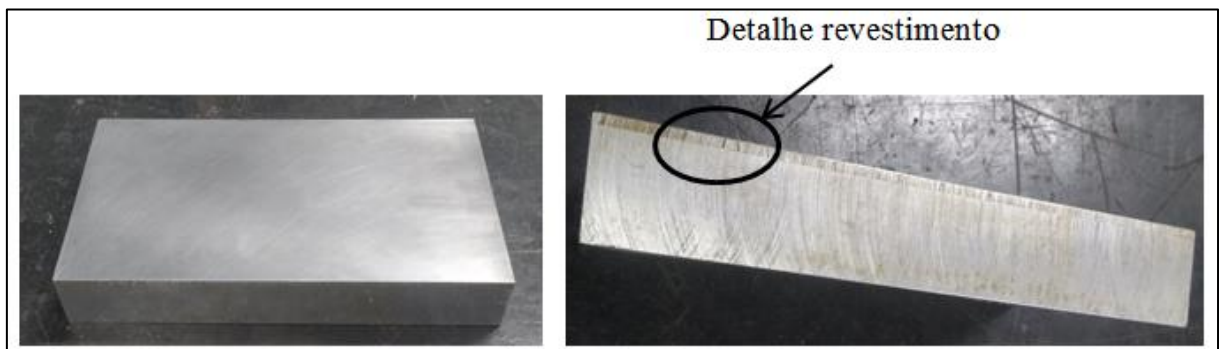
Chapa de aço ABNT 1045 revestida com Babbitt após usinagem de acabamento.
